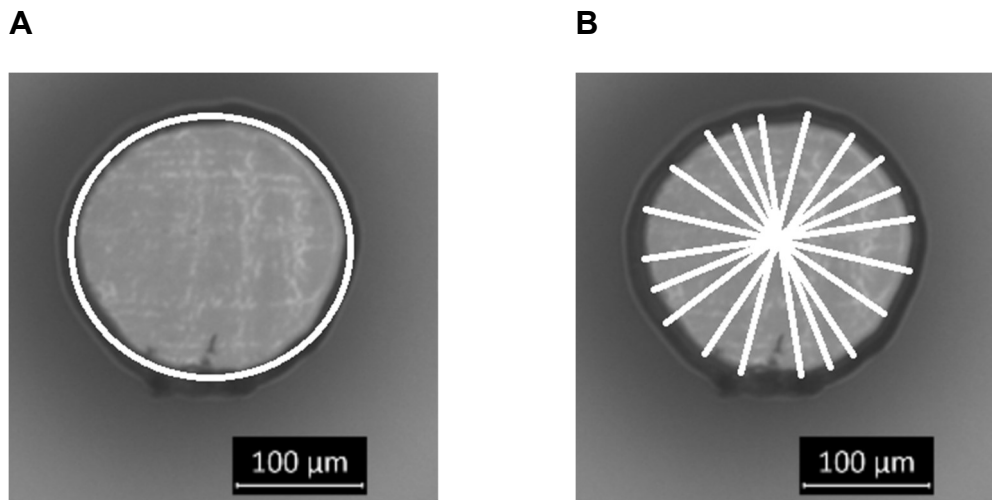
Aufnahme von einem Zylinder durch das Stereomikroskop in der Draufsicht mit einer Soll-Bemaßung der Grundfläche des Kreises von 400 µm Durchmesser. A: Mit weißem angepasstem Mess-Oval, um den Flächeninhalt des Kreises zu berechnen. B: Mit 10 weißen Linien, die sternförmig angeordnet sind, um den Durchmesser des Kreises zu bestimmen.
